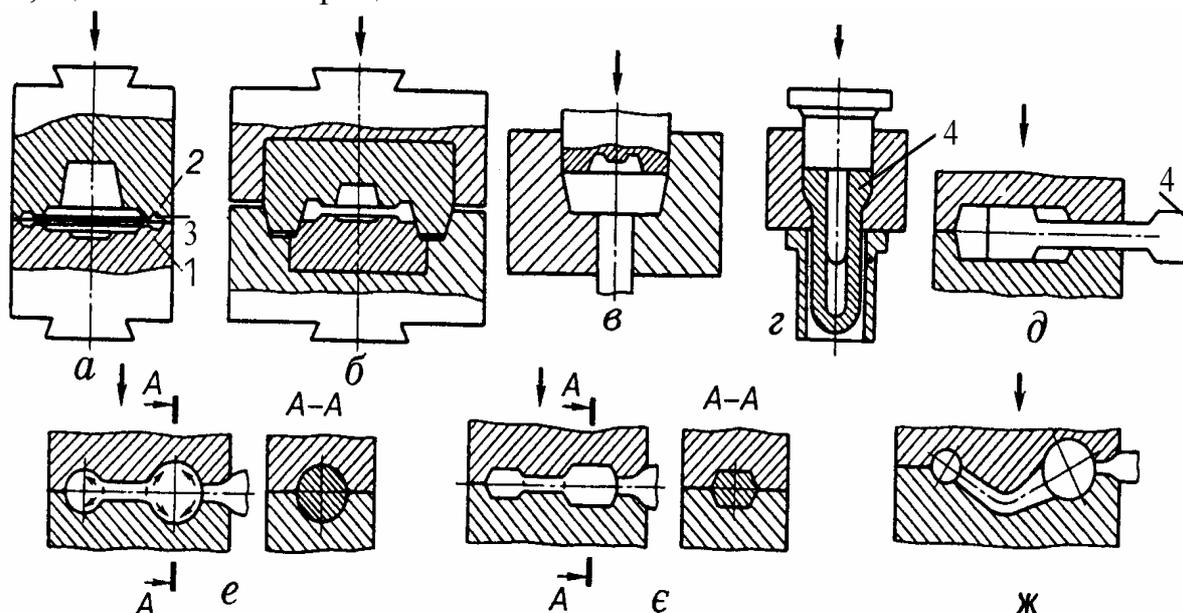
Схеми гарячого об'ємного штампування і заготовельних рівчаків
